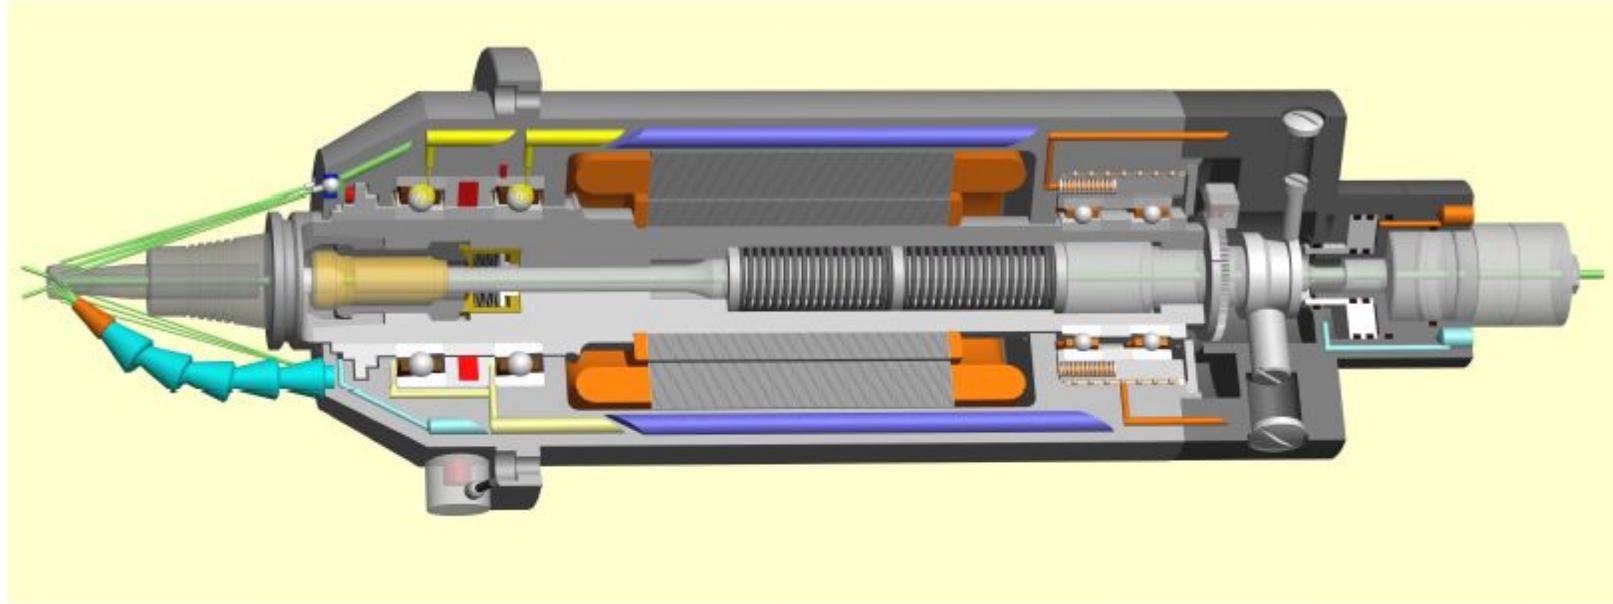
HF- моторшпиндель с оснащением «Condition Monitoring» - датчиками и исполнительными элементами для контроля процесса высокоскоростной обработки
